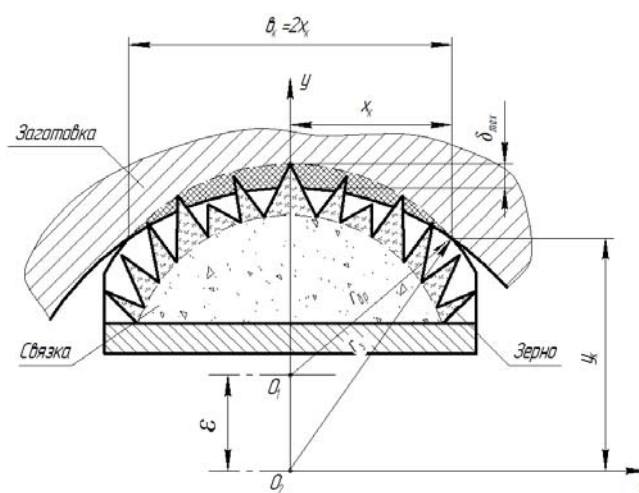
Геометрическая схема внедрения алмазных зерен бруска в поверхность заготовки
